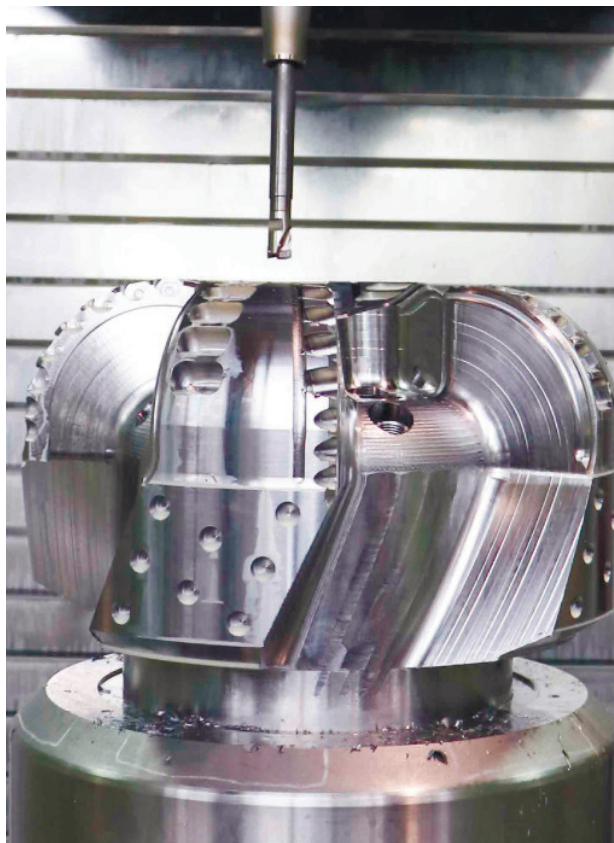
Долото в процессе изготовления в обрабатывающем центре
